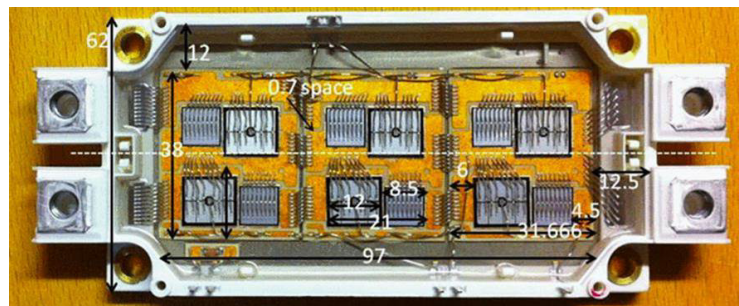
Draufsicht eines Rahmenmoduls mit drei DCBs [35]
